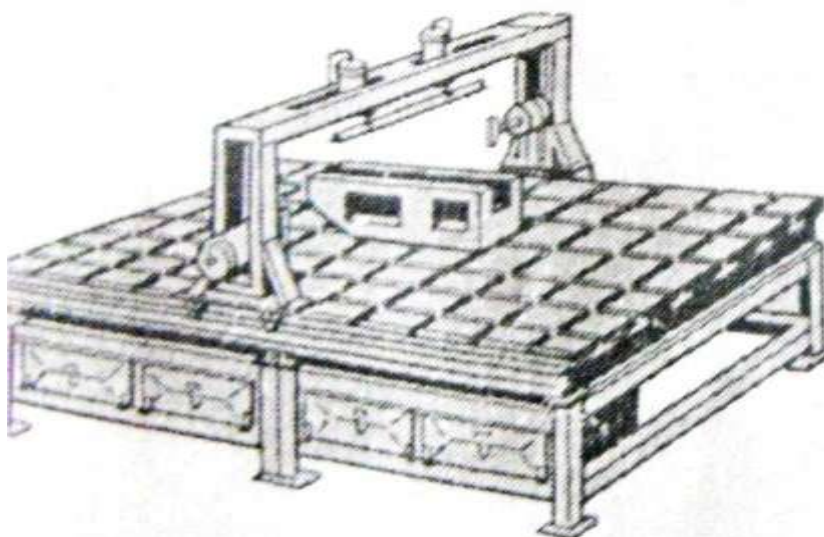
Универсальный стенд для сборки узлов сварных конструкций.
